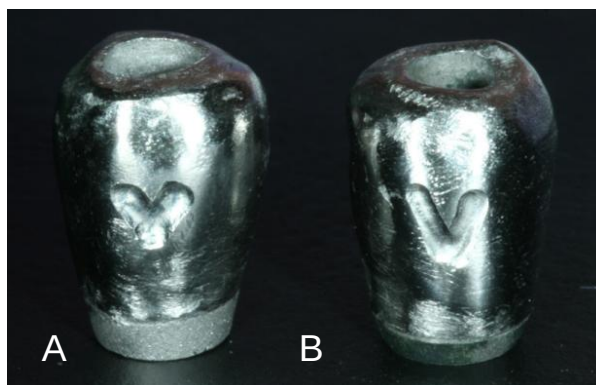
Pilar Calcinável (A); Pilar Sobrefundido (B).
